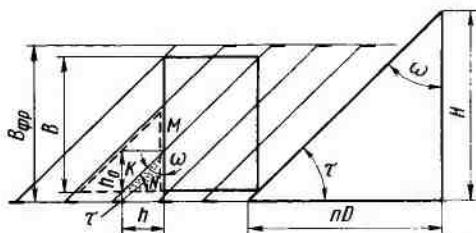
Развертка поверхности резания при работе цилиндрической фрезой с винтовым зубом
